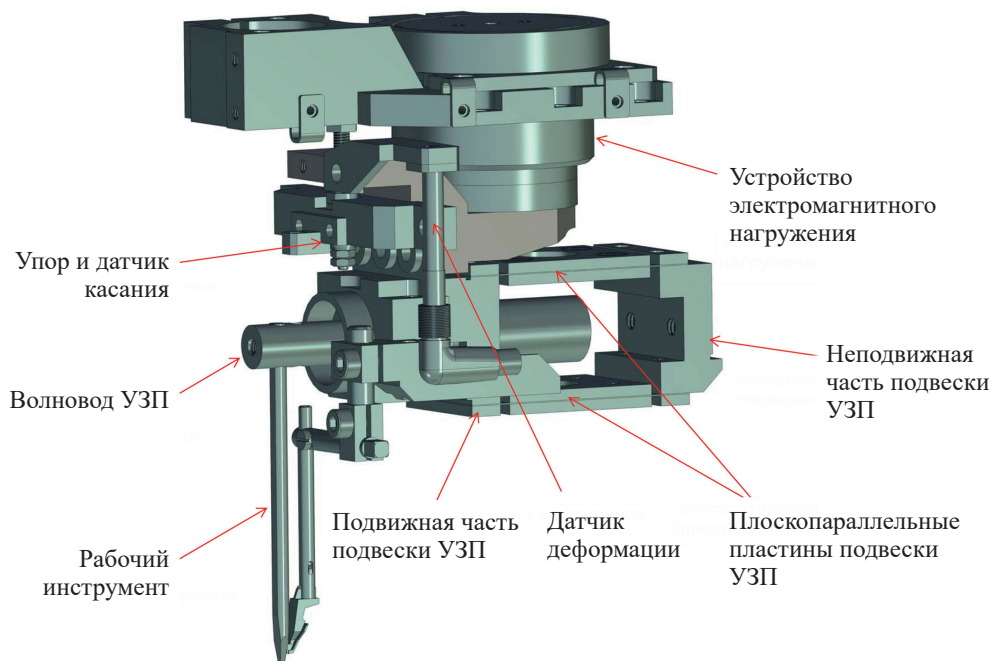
Основные части ультразвуковой сварочной головки
